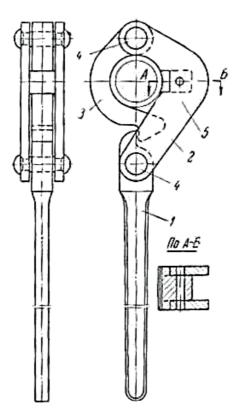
Шарнирный ключ: 1 – рукоятка; 2, 3 – откидные скобы; 4 –соединительные оси; 5 – сухарь
